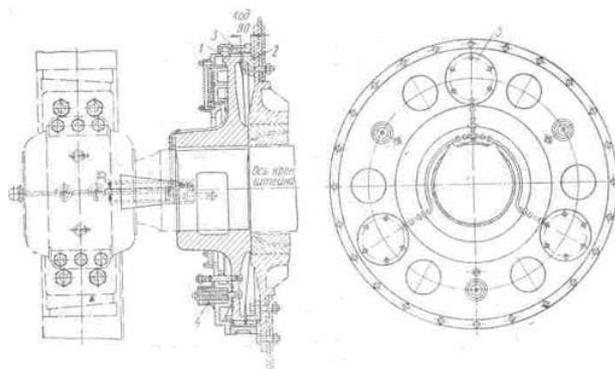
Зубчатый механизм перестановки с пружинно-пневматическим приводом
